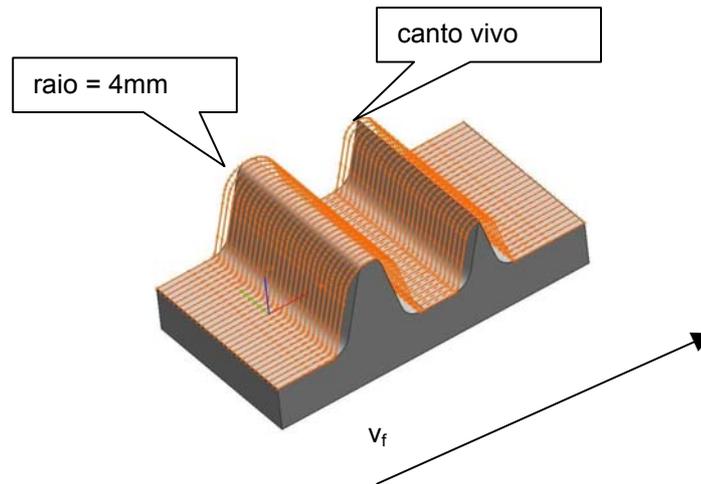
Geometria da peça usinada e direção de avanço da usinagem.
